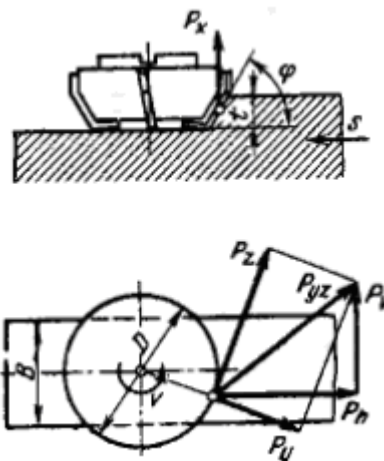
Силы резания при фрезеровании торцевой фрезой
